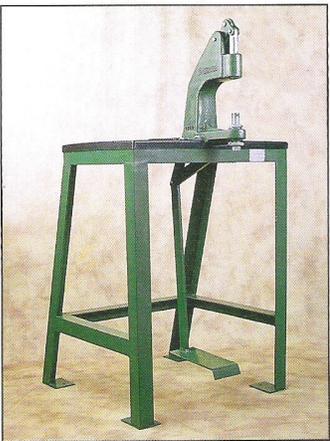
Máquinas que fabrica DLK Industrias. Fuente: Catálogo DLK Industrias.
